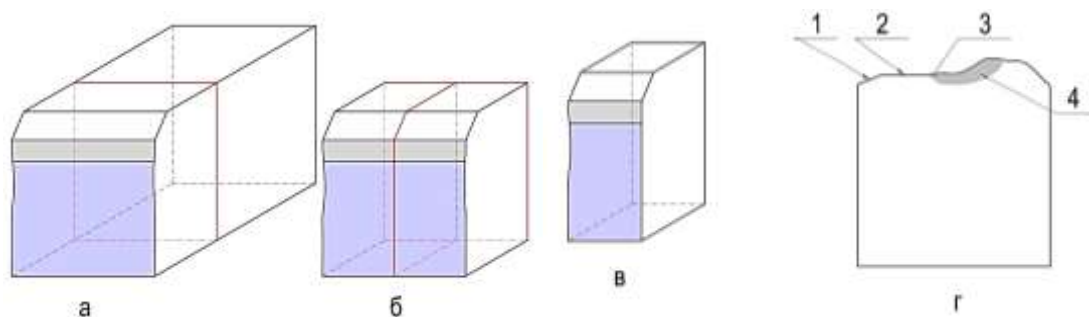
Этапы подготовки образца для измерений микротвердости в ЗПД: а – общий вид половинки разрушенного образца с нанесенной разметкой для вырезки фрагмента, содержащего излом; б – фрагмент образца, содержащего его излом и разметка для дальнейшей резки; в – общий вырезанного фрагмента образца; г – поверхность фрагмента образца, подготовленная для измерения микротвердости: 1 – надрез, 2 – усталостная трещина, 3 – место старта динамической трещины, 4 – область исследования зоны в области старта динамической трещины.
